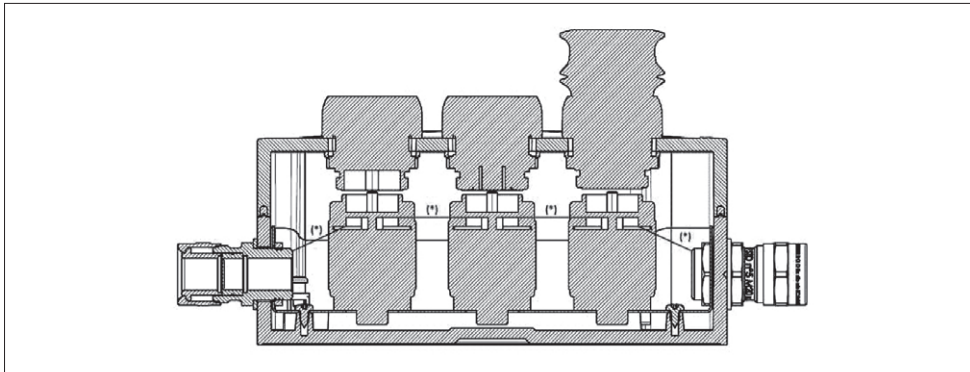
Detalles de las distancias de tolerancia y montaje del prensaestopas metálico
